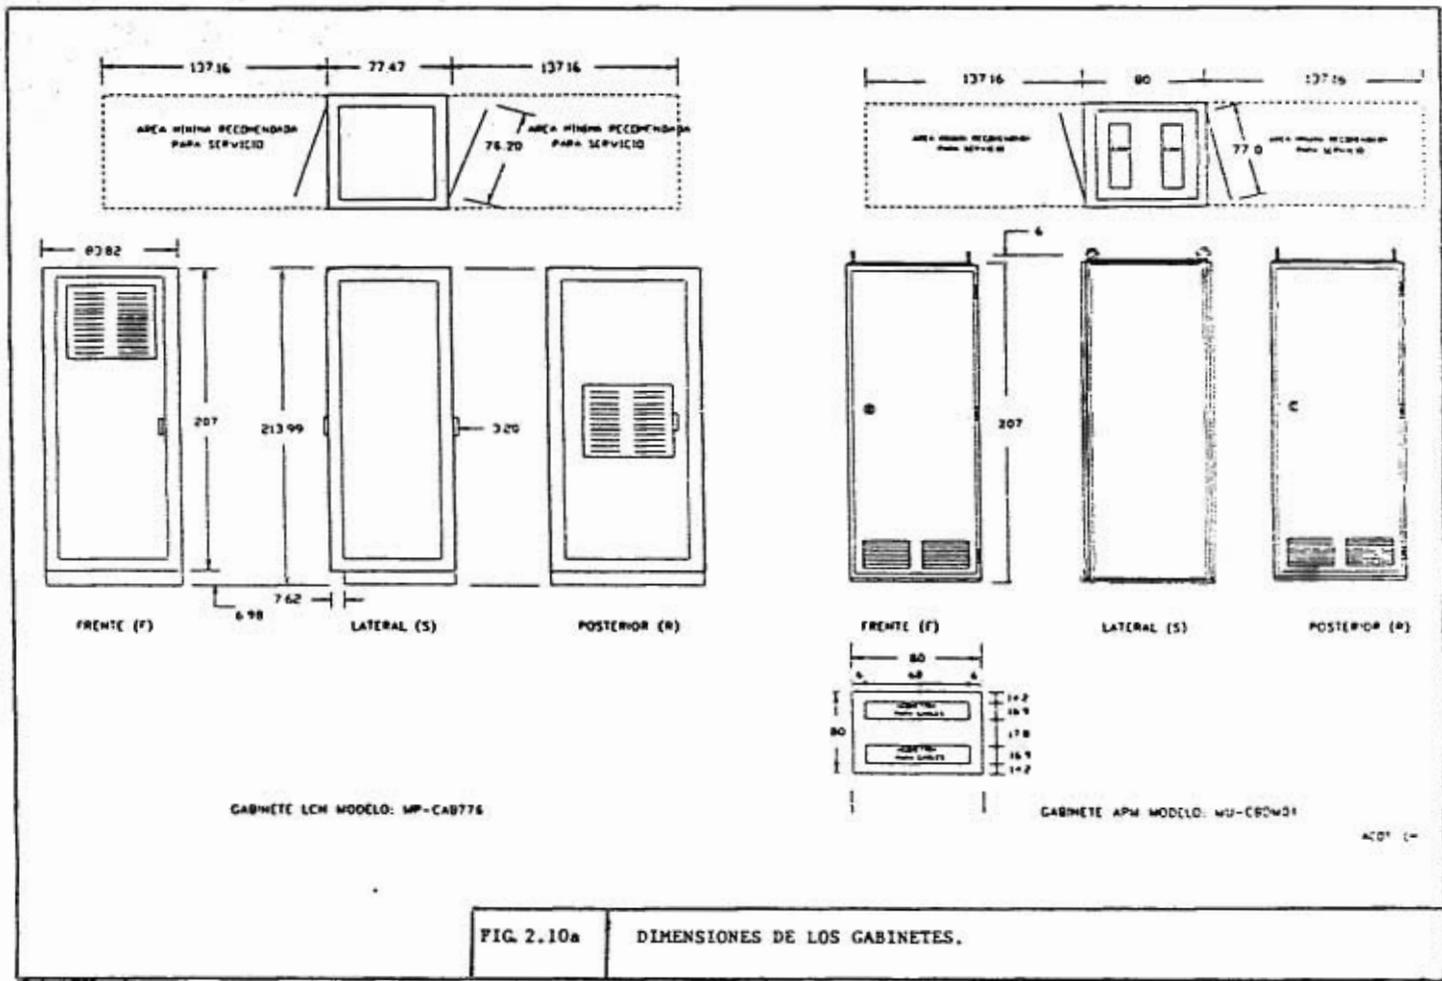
DIMENSIONES DE LOS GABINETES.
